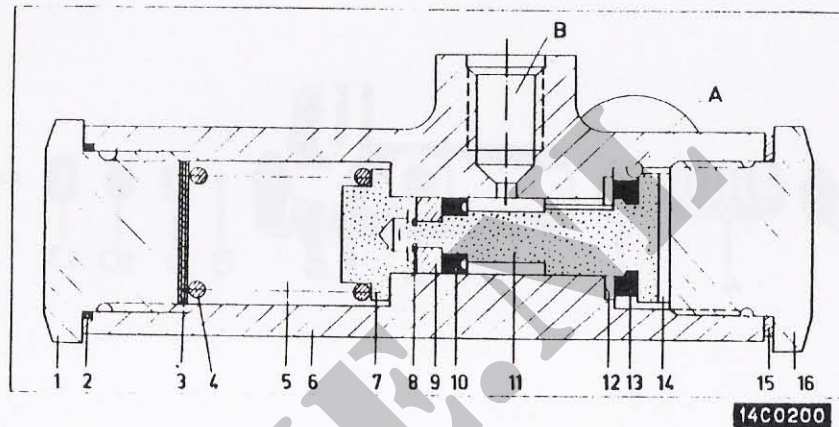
Voetremmechanisme (doorsnede rempedaalas)
